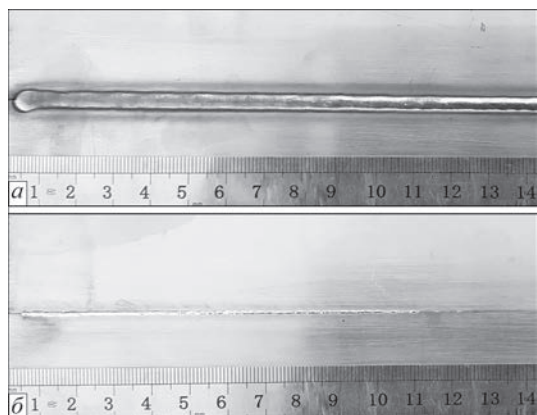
Зовнішній вигляд стикового з'єднання сталі SUS304 ($\delta = 3,0$ мм): *a* – верхній валик; *b* – корінь шва
